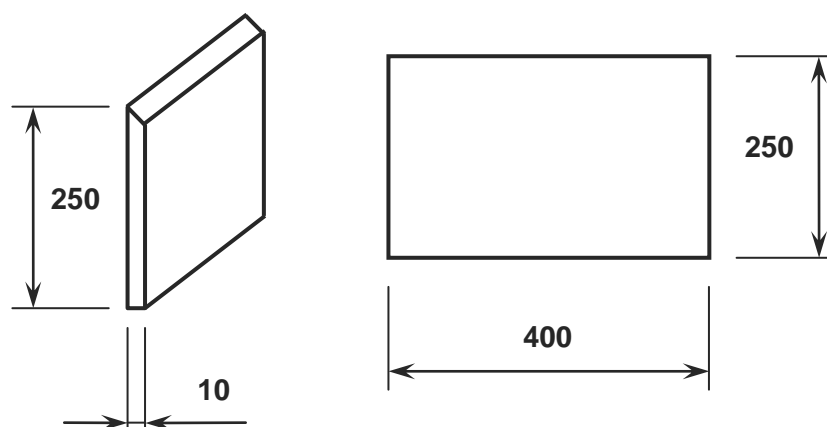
Размеры конструкции прямоугольного водослива с тонкой стенкой
